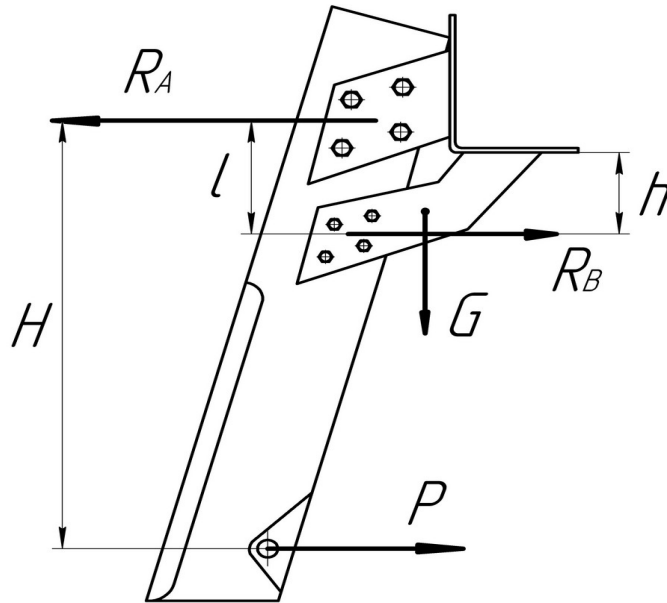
Схема дії сил, що діють на зварне з'єднання
